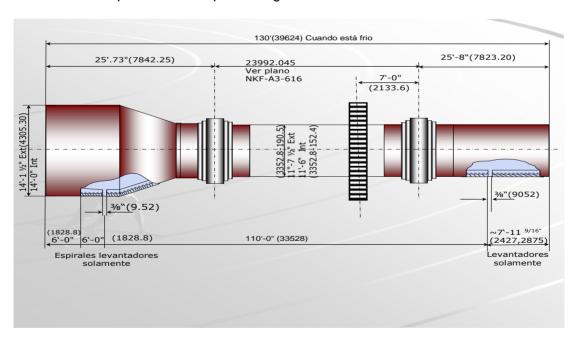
Cuerpo cilíndrico del horno rotatorio de secado de mineral con posición horizontal.
